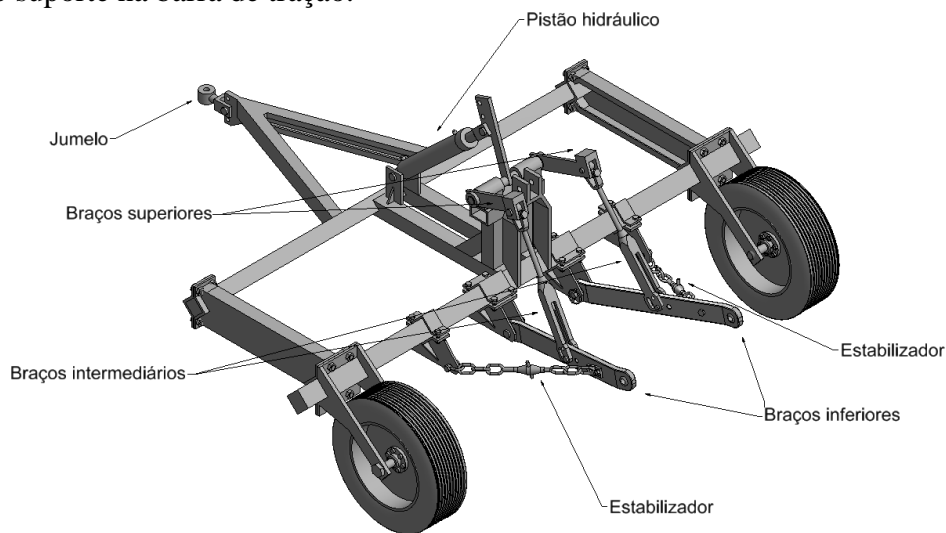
Vista isométrica superior/esquerda e componentes.
